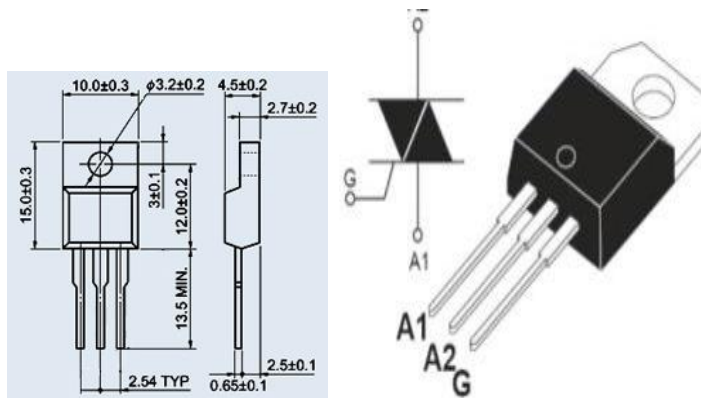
Габаритні розміри тиристора типу VT136-600E
